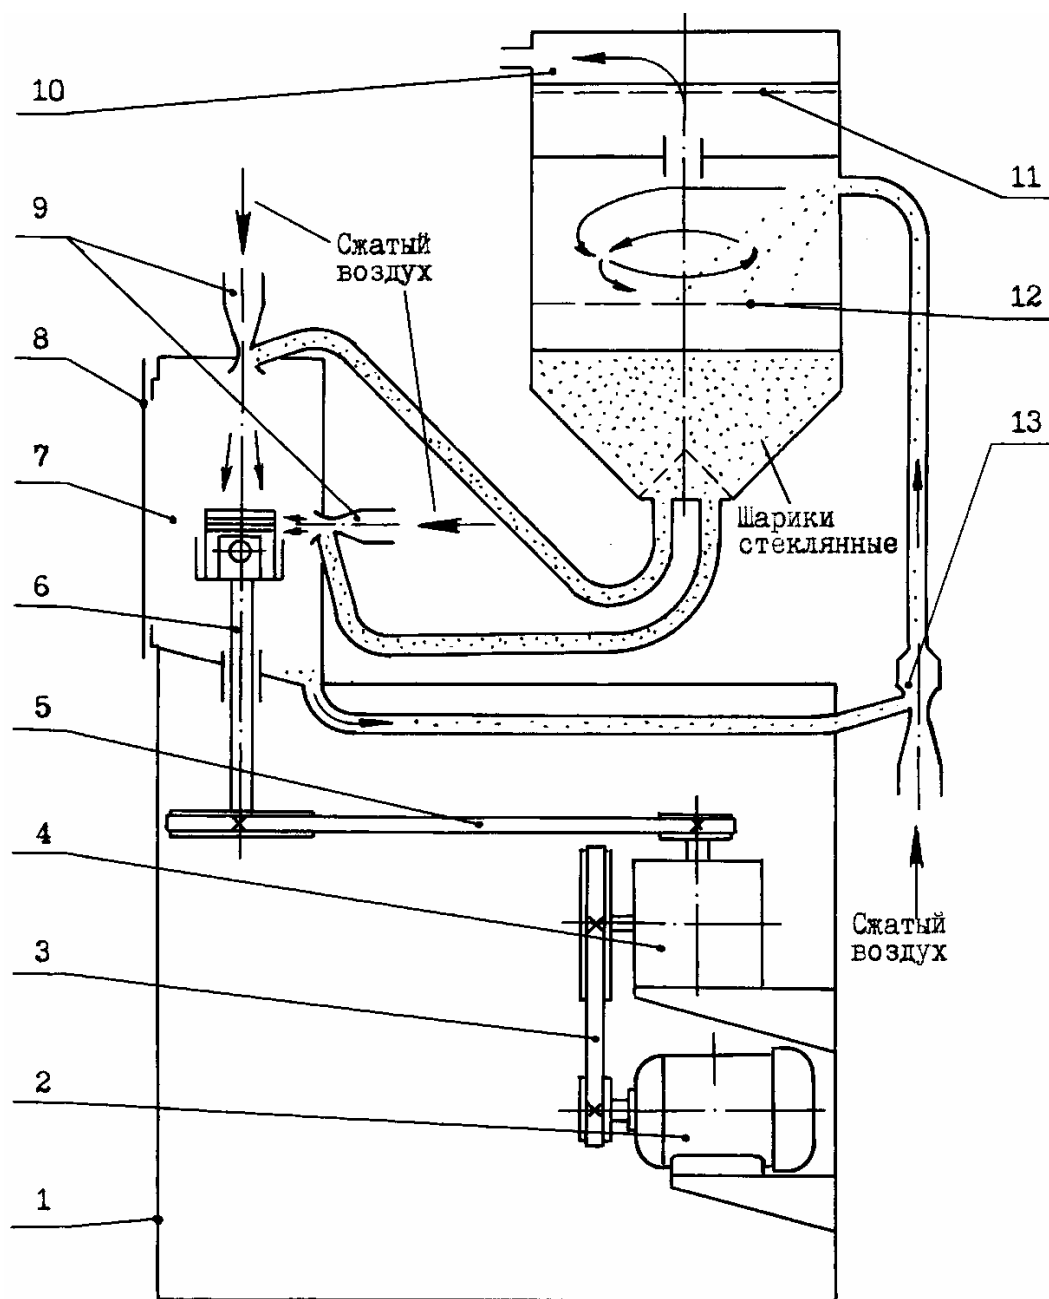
Схема машины для очистки деталей потоком стеклянных шариков: 1 – корпус; 2 – электродвигатель; 3 и 5 – ременные передачи; 4 – редуктор; 6 – вал; 7 – камера; 8 – дверь; 9 – эжекционные форсунки; 10 – сборник-фильтр; 11 – матерчатый фильтр; 12 – сетка; 13 – эжектор
